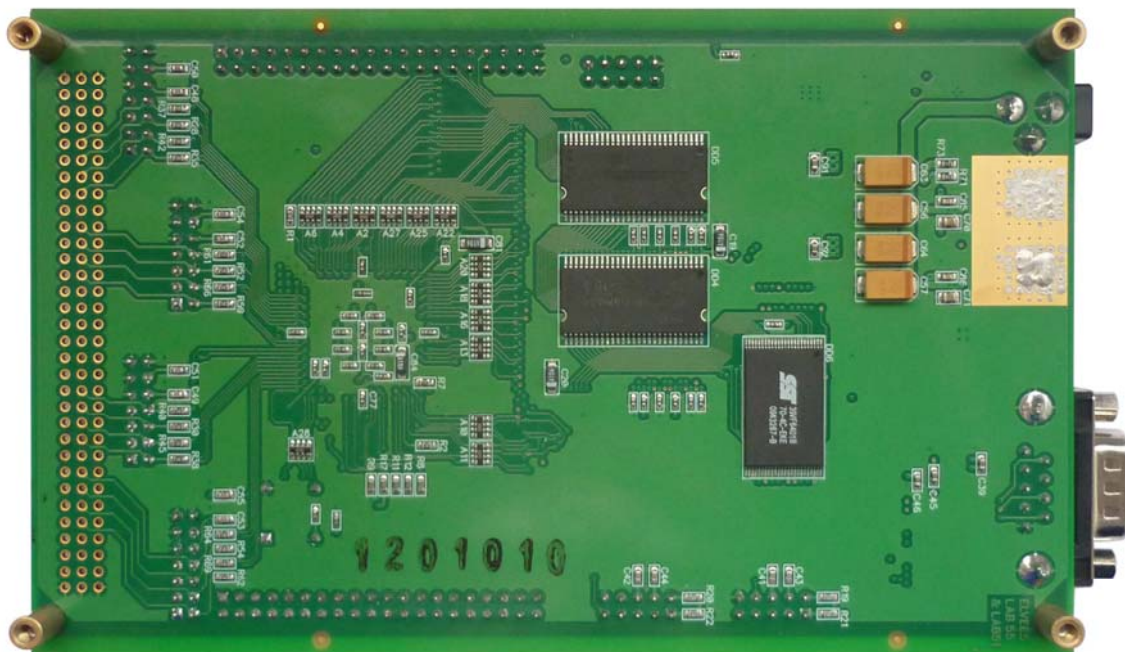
Внешний вид отладочного модуля. Обратная сторона платы.
